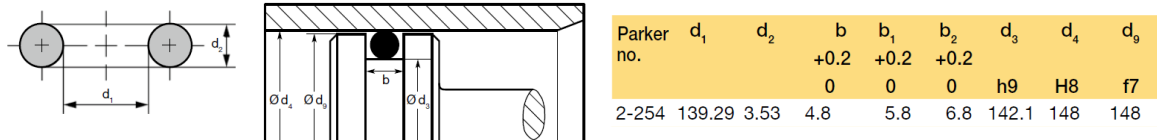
Dimensões O-Ring Parker® 2-254 [63]
